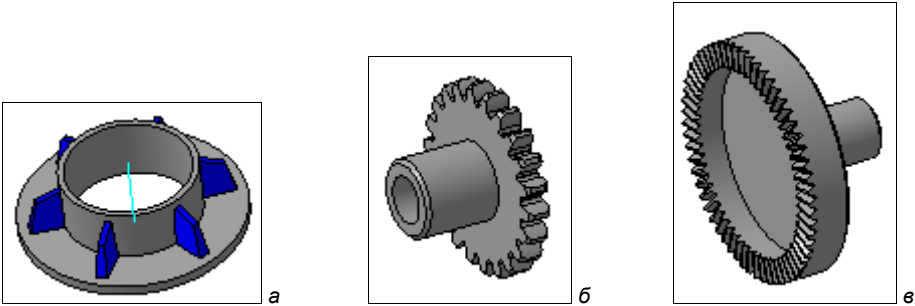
а — Модель 10 с ребрами; б — зубчатое колесо 22; в — зубчатая полумуфта
